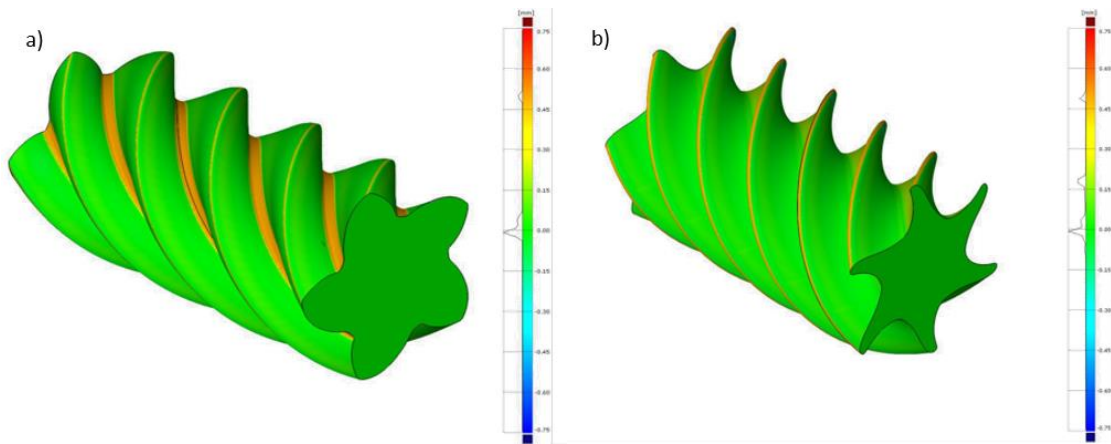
Desviación dimensional estimada del Demostrador IV: a) Compresor de tornillo sin fin macho no simétrico y b) Compresor de tornillo sin fin hembra no simétrico.
